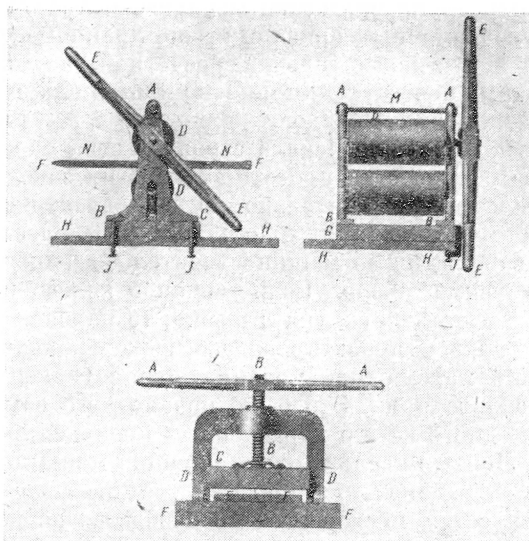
Прокатный печатный станок и печатный пресс конструкции Уатта
